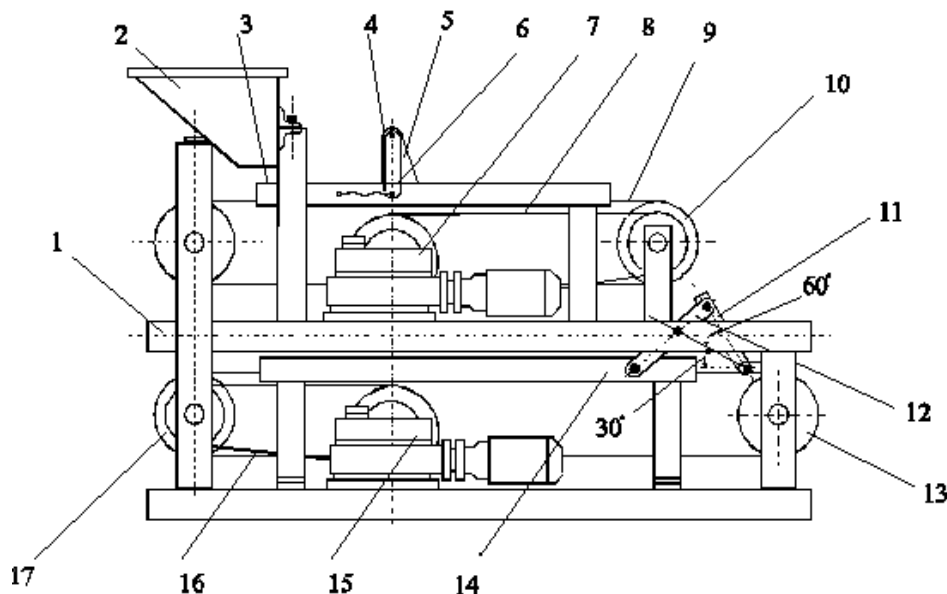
Схема устройства для сортировки пищевых отходов: 1 – корпус; 2 – дозирующий бункер; 3 – верхний транспортер; 4 – П-образная рама; 5 – пружина растяжения; 6 – металлическая планка; 7 – силовая установка; 8 – ведущий барабан; 9 – клиновидный ремень; 10 – лента верхнего транспортера; 11 – металлическая планка; 12 – стойка; 13 – нижний транспортер; 14 – ведомый барабан; 15 – силовая установка; 16 – клиновидный ремень; 17 – привод ведущего барабана.
